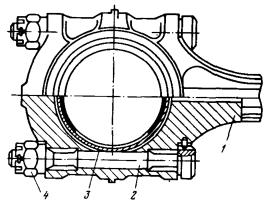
Большая головка шатуна компрессора 4ВМ10-100/8:
